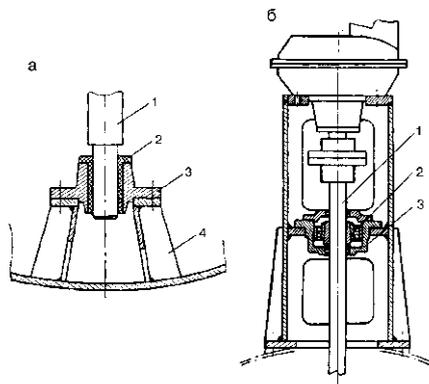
Конструктивные схемы установки валов мешалок:
